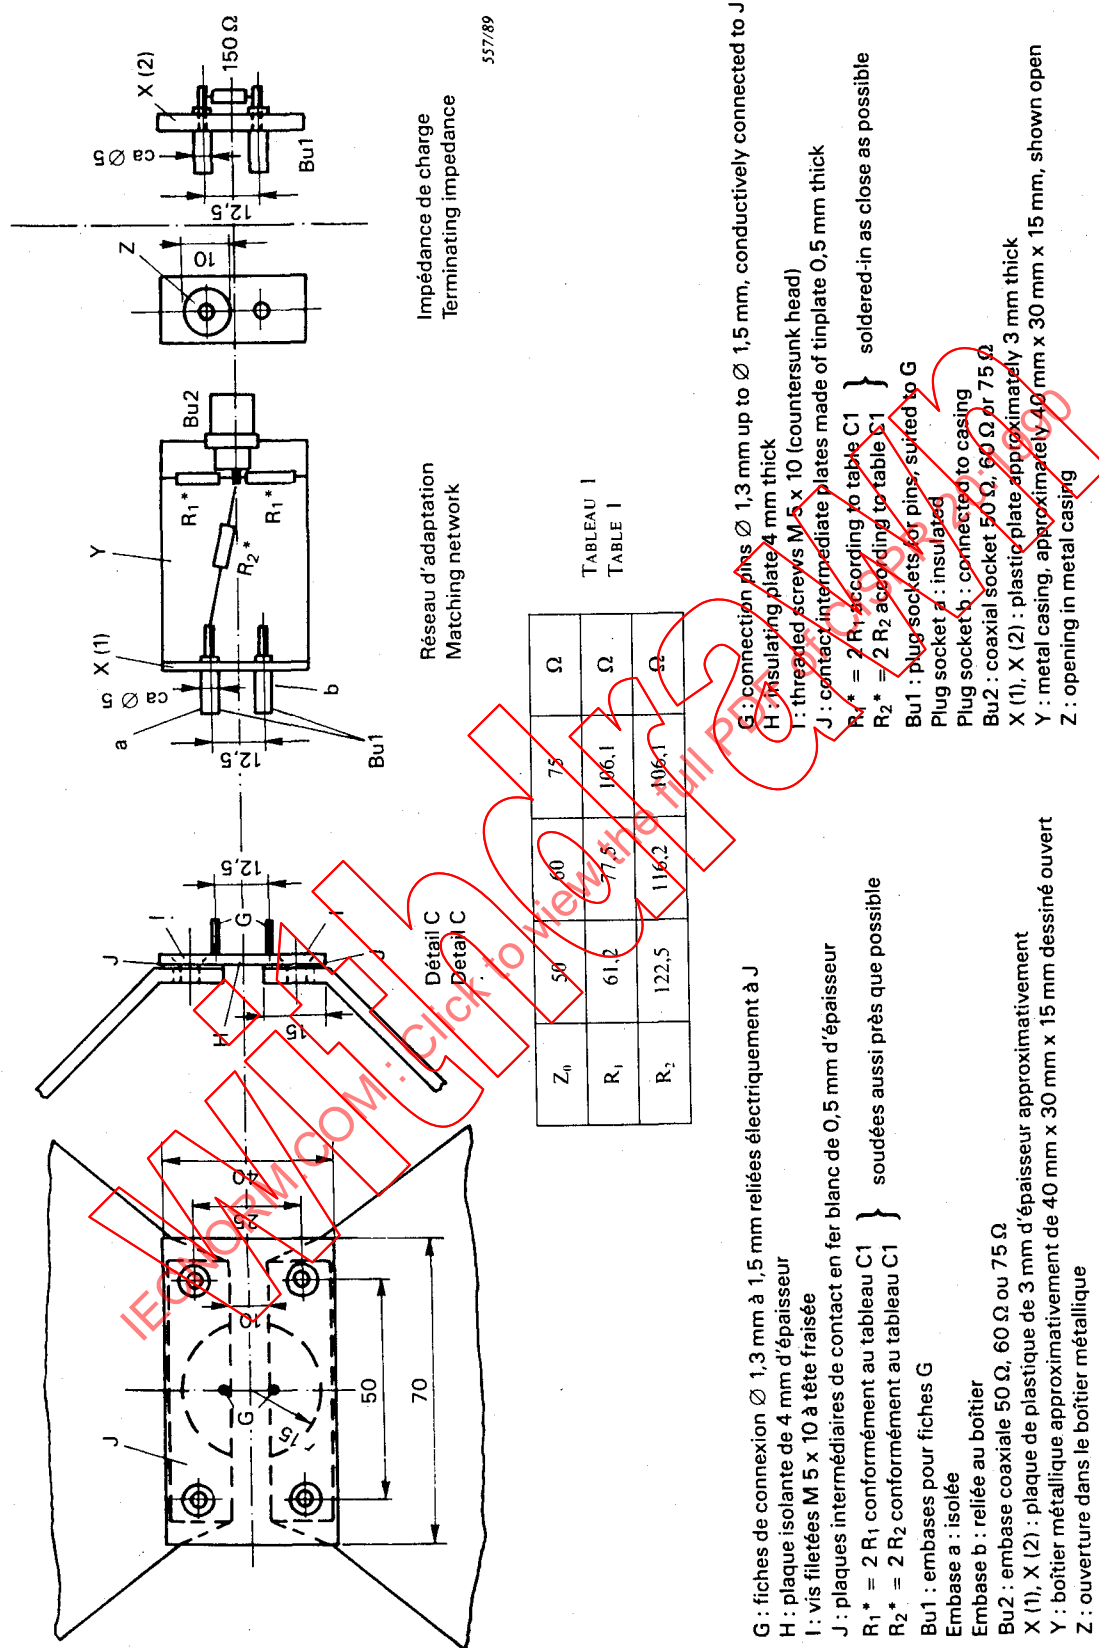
Détails de construction d'un dispositif TEM à ligne ouverte (voir 5.2.2)
